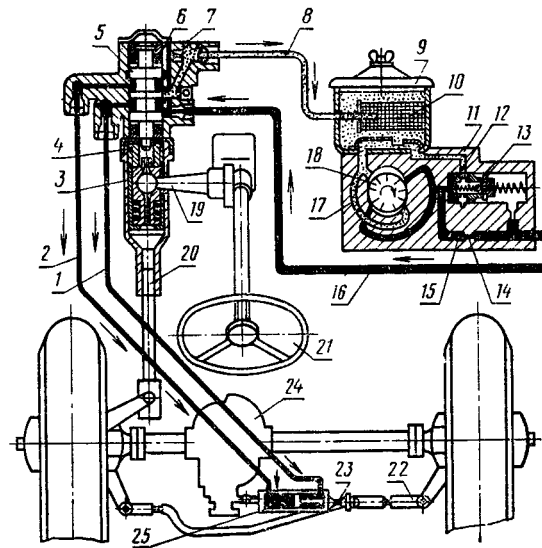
Схема гидроусилителя рулевого управления автомобиля ГАЗ-66:
